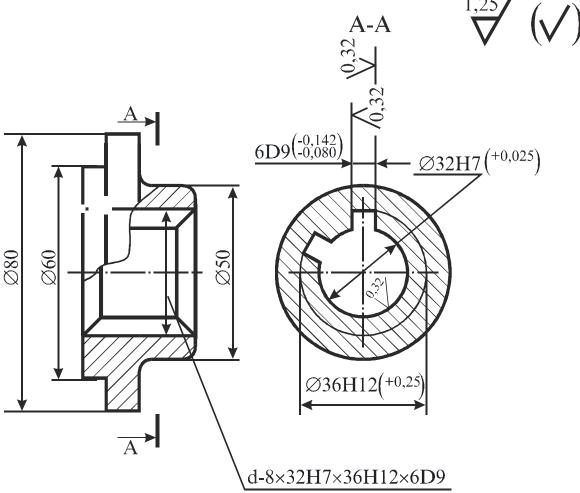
Пример оформления рабочего чертежа шлицевой втулки
